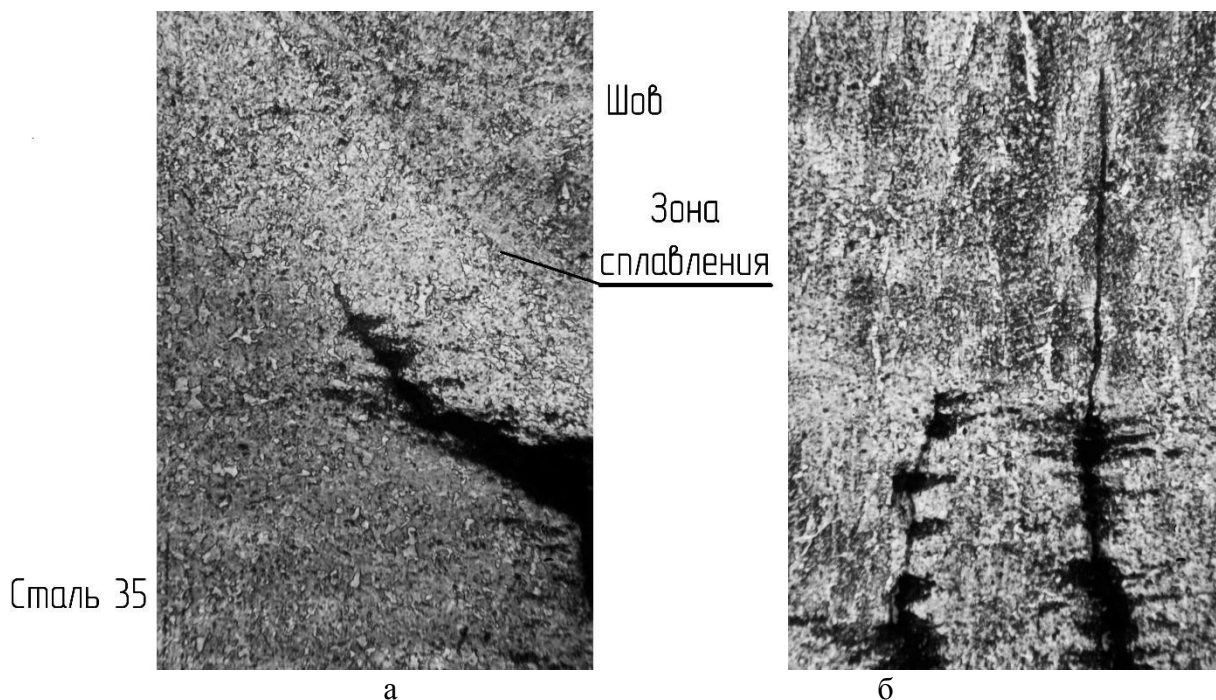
Микротрещины в сечении неразрушенного сварного соединения вала: а – зона сплавления сталь 35 – шов, б - зона сплавления сталь 42 Cr Mo – шов
